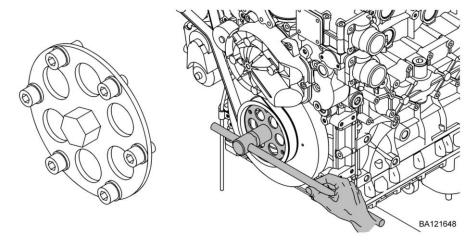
Dispositivo de giro: montaje de la polea de transmisión - árbol del cigüeñal, herramienta especial nº 30a
